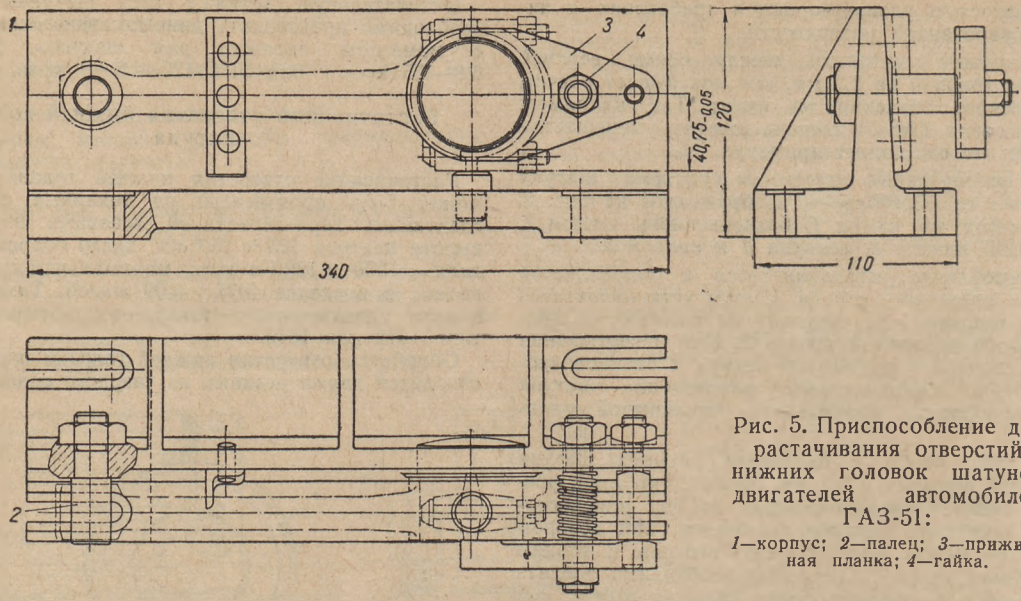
Приспособление для растачивания отверстий нижних головок шатунов двигателей автомобилей ГАЗ-51:
